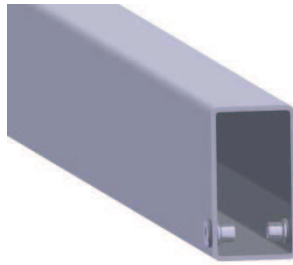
Perfil de acero cerrado de sección rectangular con tuercas remaches
